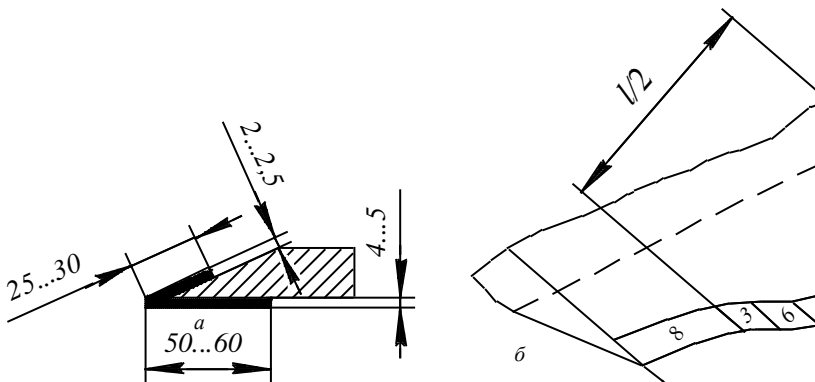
Схема наплавки полукруглой режущей кромки экскаваторных ковшей
